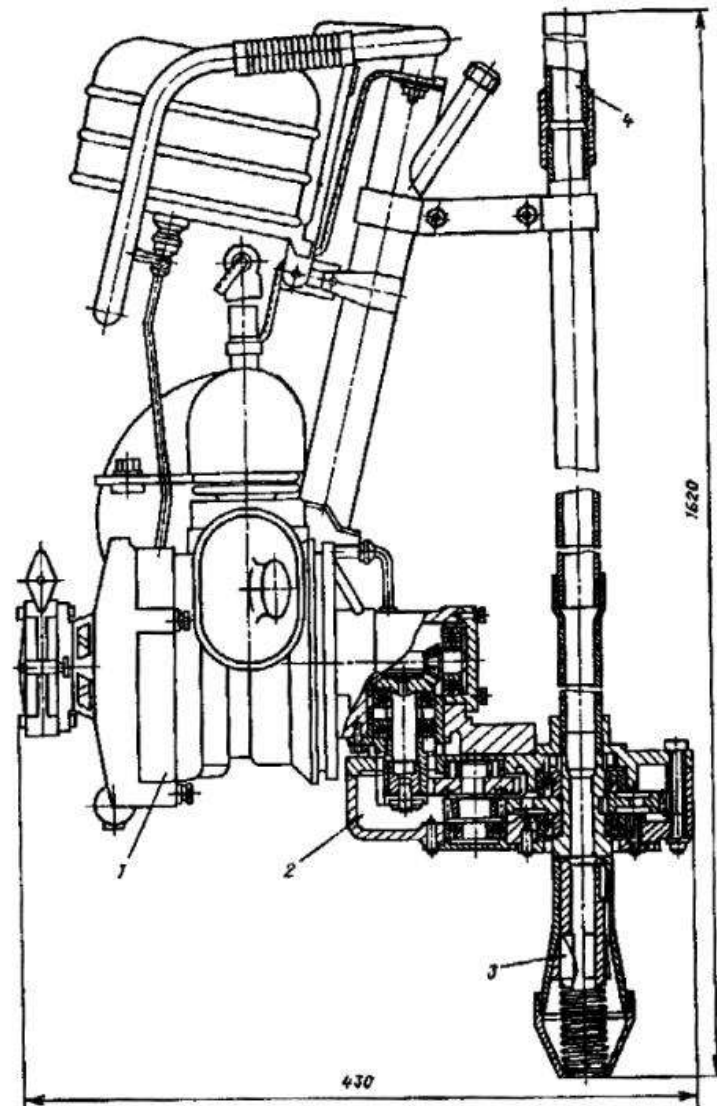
Приспособление ПЗД для ввертывания электродов заземления:
